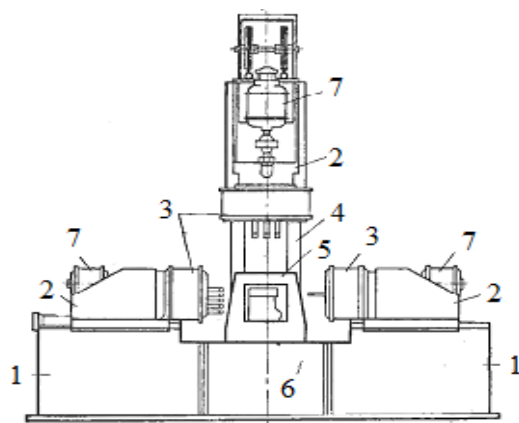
Загальний вигляд тристороннього свердлильного верстата
